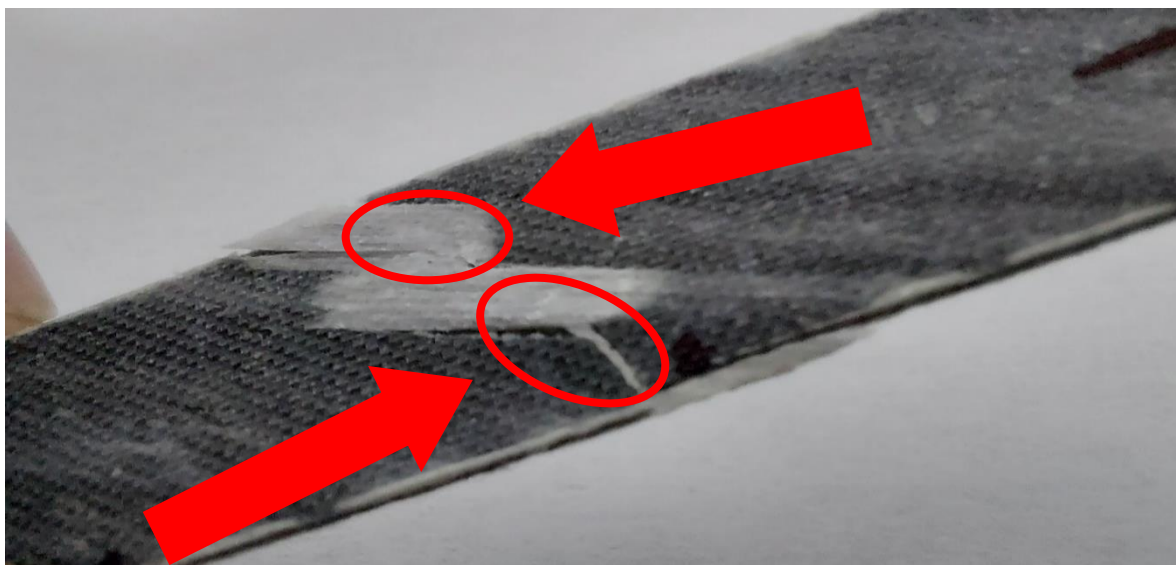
Fractura de la probeta FT5 del laminado $[26/0_4/26]$.
